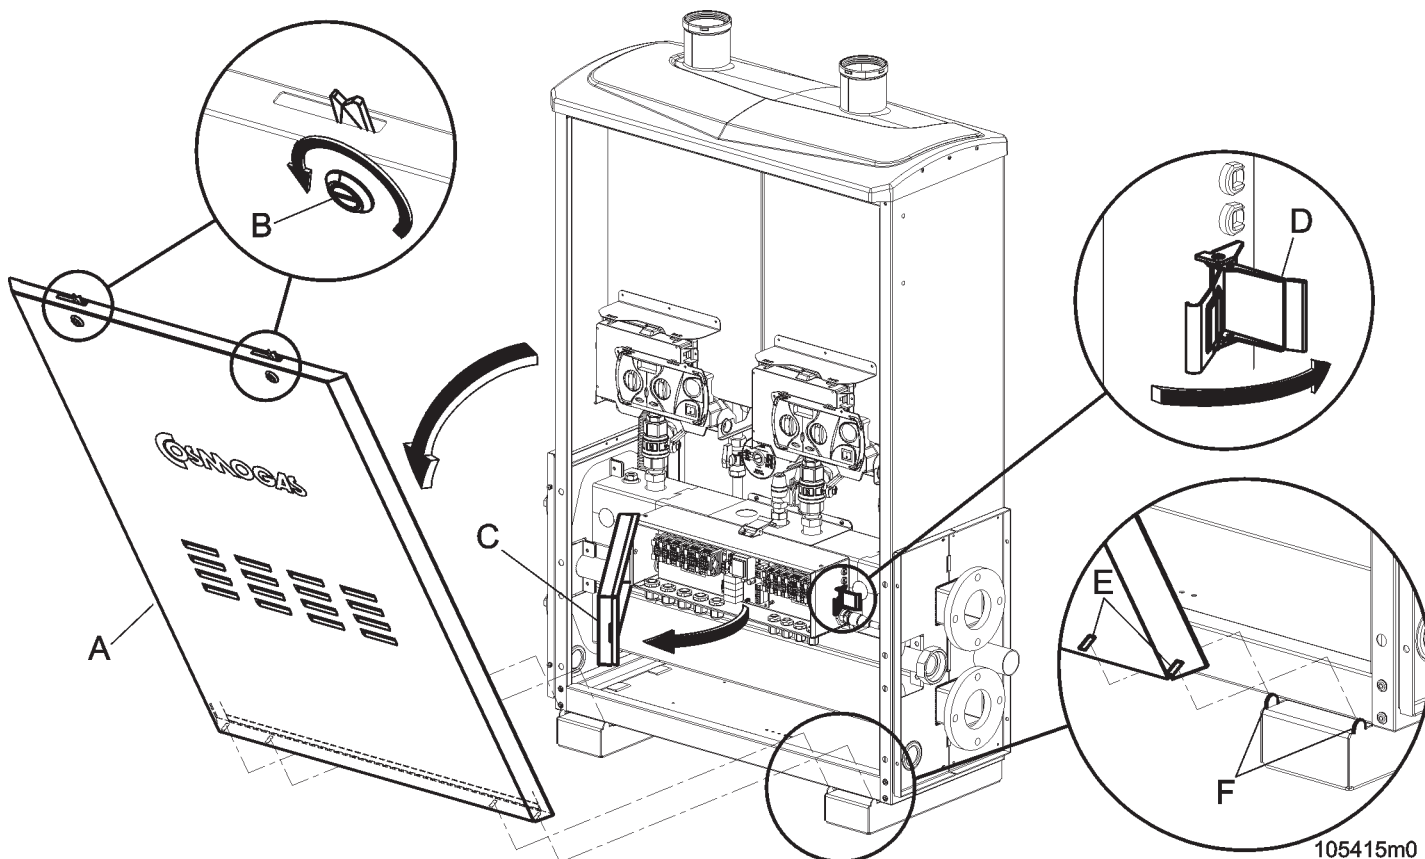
Montaggio e smontaggio della mantellatura e accesso ai componenti interni
